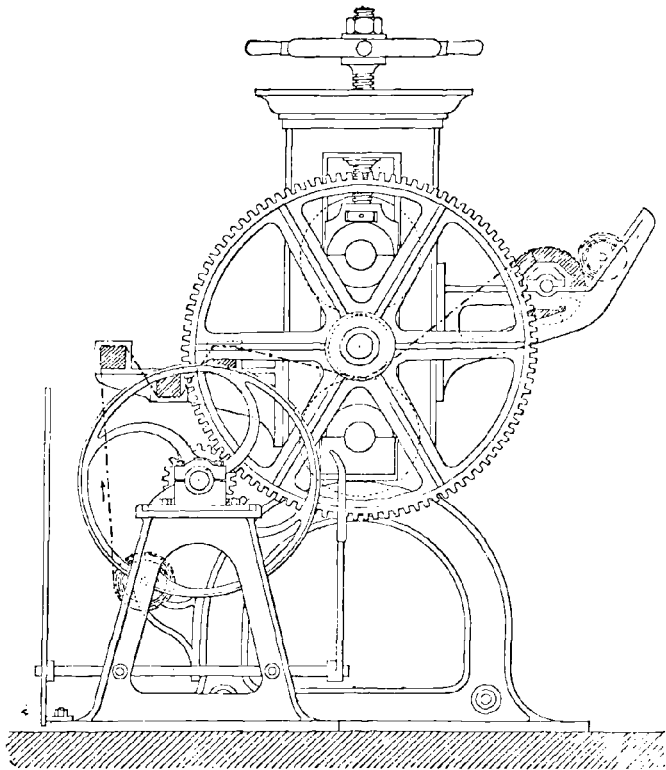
Machine à gaufre (construction Welter, de Mulhouse).
